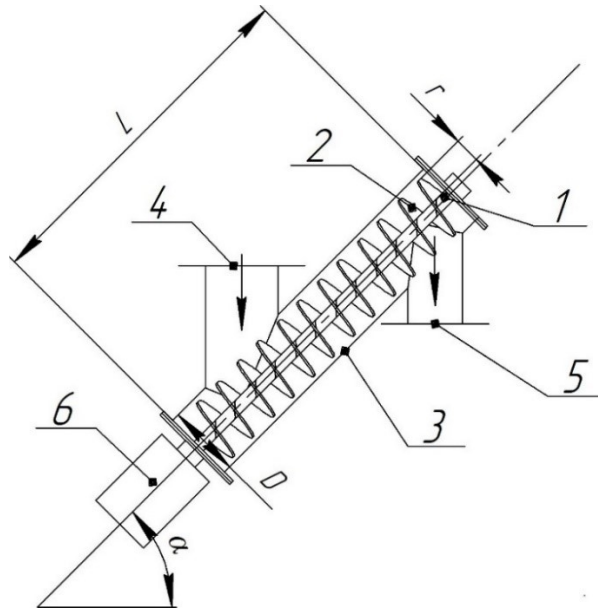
Схема шнекового транспортер: 1 – вал; 2 – лопасти; 3 – корпус; 4,5 – входной и выходной патрубок; 6 – привод
